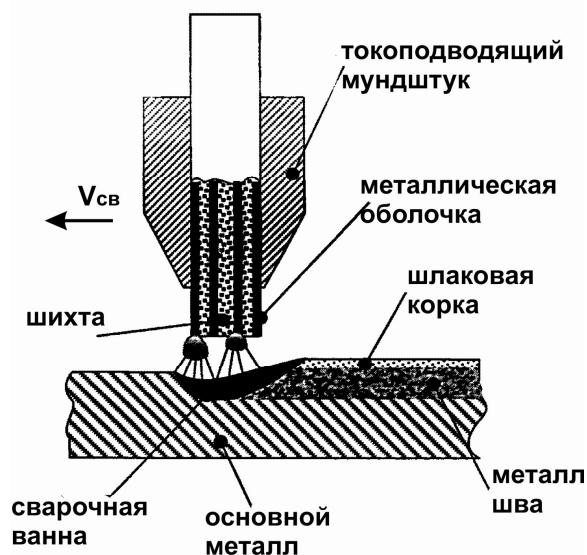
Схема процесса сварки порошковой проволокой
